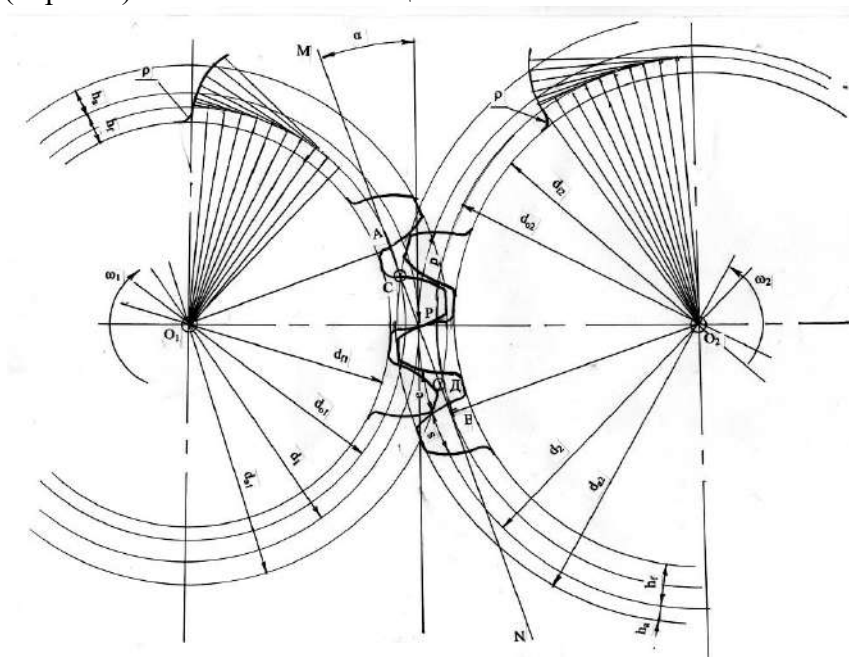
Эвольвентное зацепление зубчатых колес
